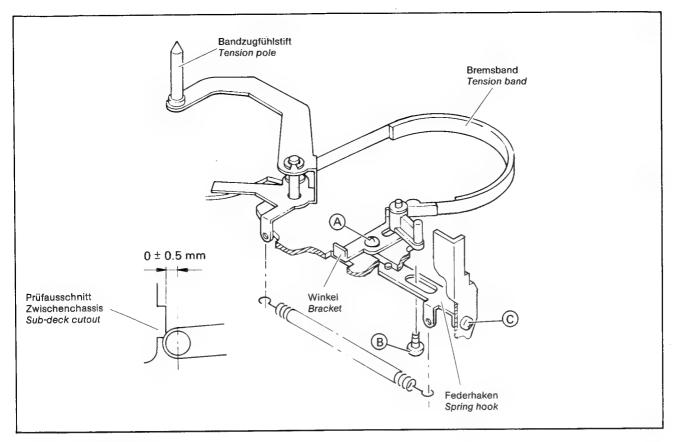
Bremszugmechanik Fig. 2–23 Back tension mechanism
